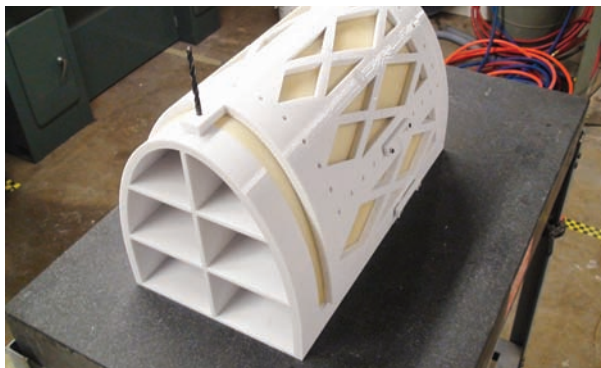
Шаблон для контроля оболочковой формы, изготовленный по технологии FDM
